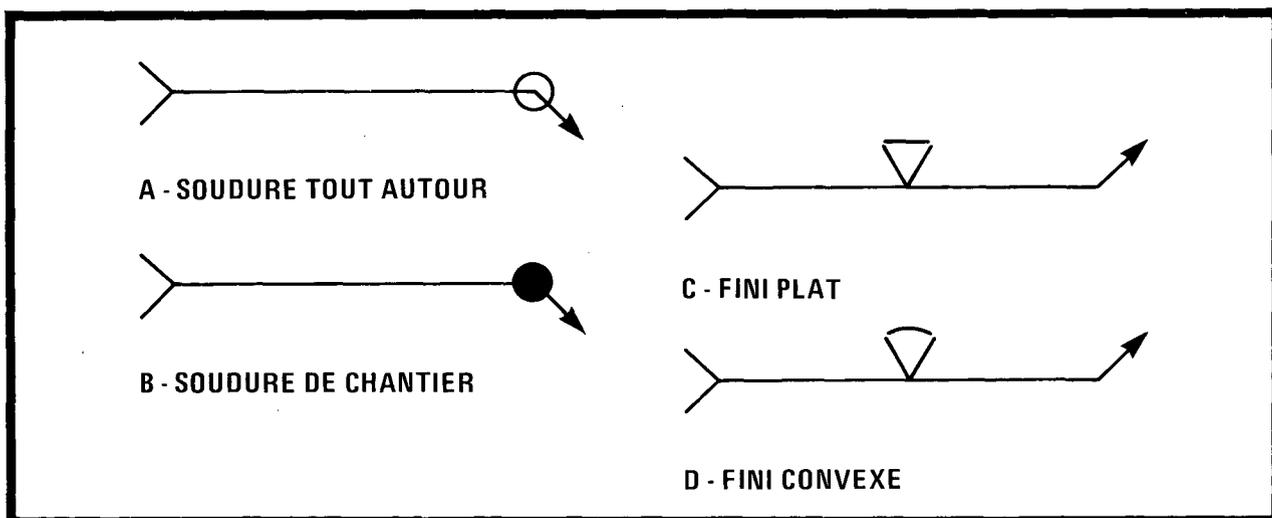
LOCALISATION ET FINIS DE SOUDAGE
